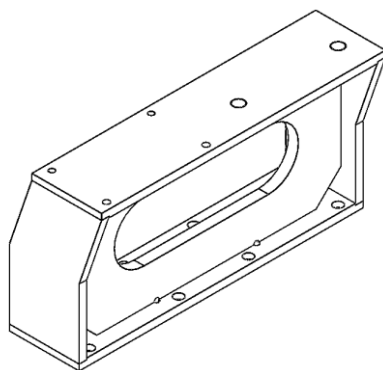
Perspectiva isométrica “Chassi suporte chumaceira CM M2 VF”.
